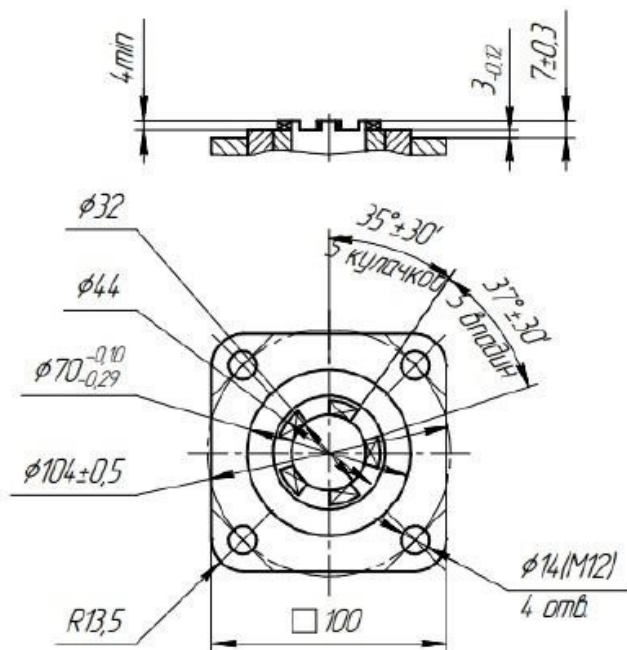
Присоединительные размеры под привод по типу АК(А)
